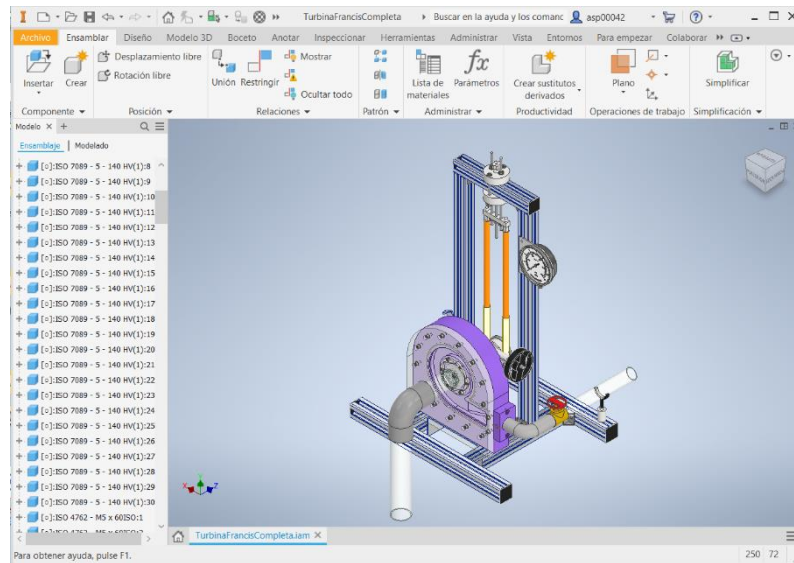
Diseño en Autodesk Inventor del conjunto Turbina Francis.
